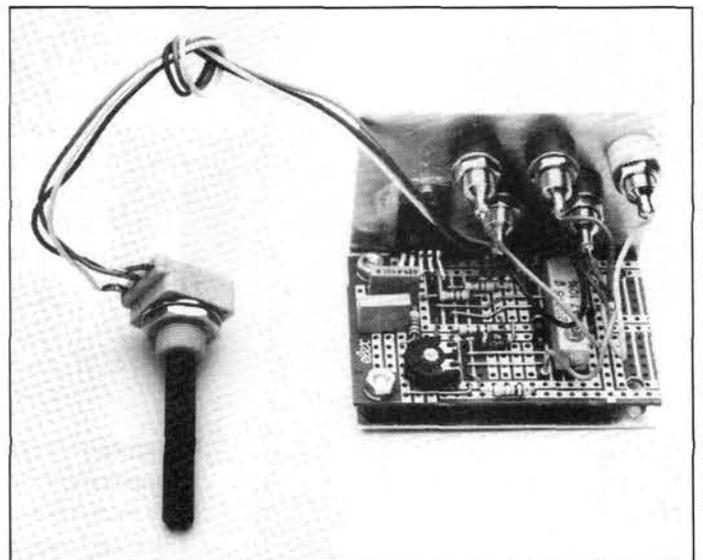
Le régulateur prêt à l'emploi. La photo montre clairement la position du circuit intégré.
